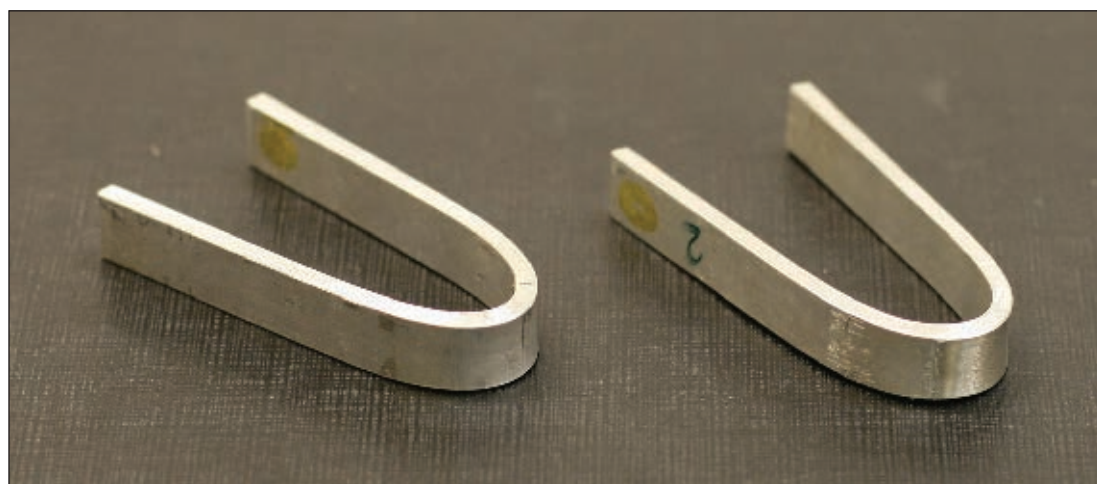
Внешний вид сварных образцов, выполненных СТП из сплава 1561, после испытаний на статический изгиб
